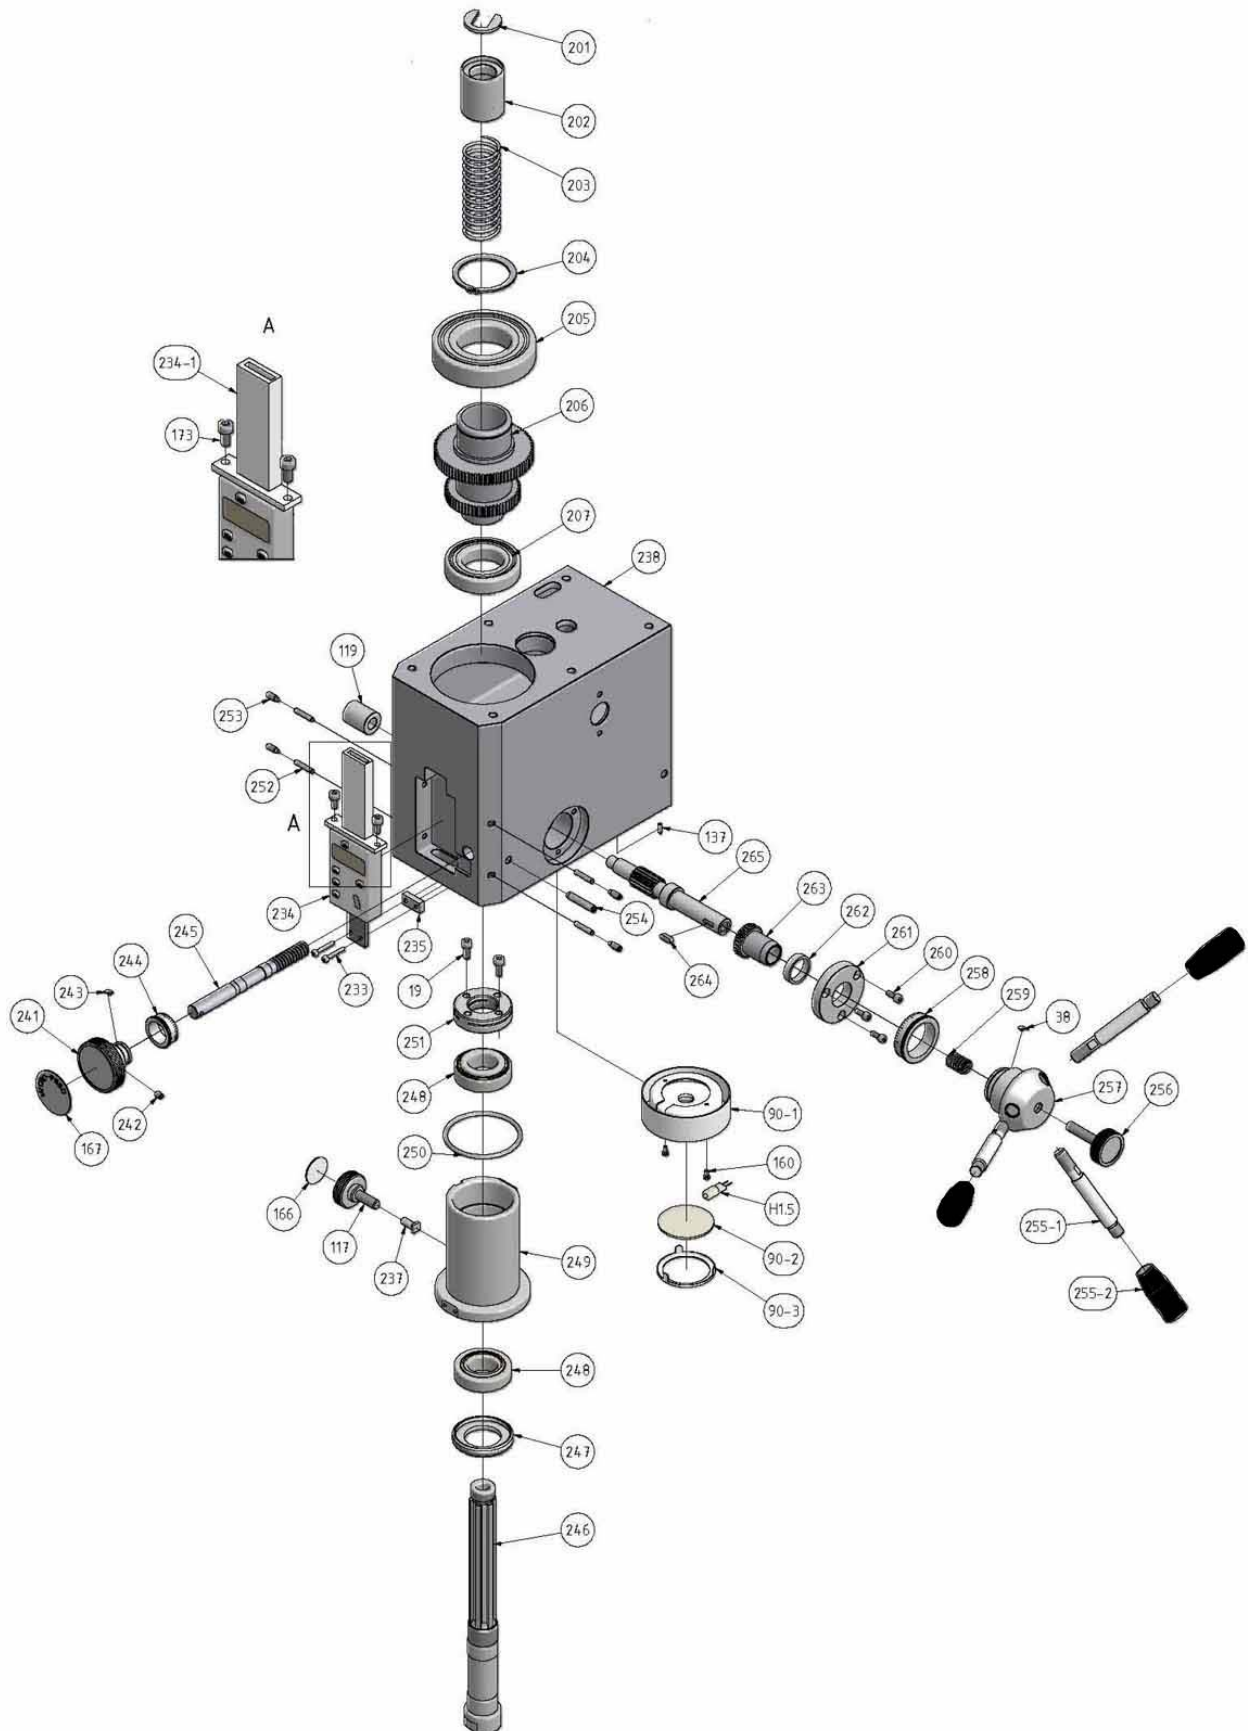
Fräskopf 2 von 2 - Milling head 2 of 2
